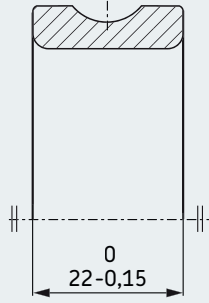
Пример указания допуска ширины внутреннего кольца радиального шарикоподшипника без доп. обозначений.
